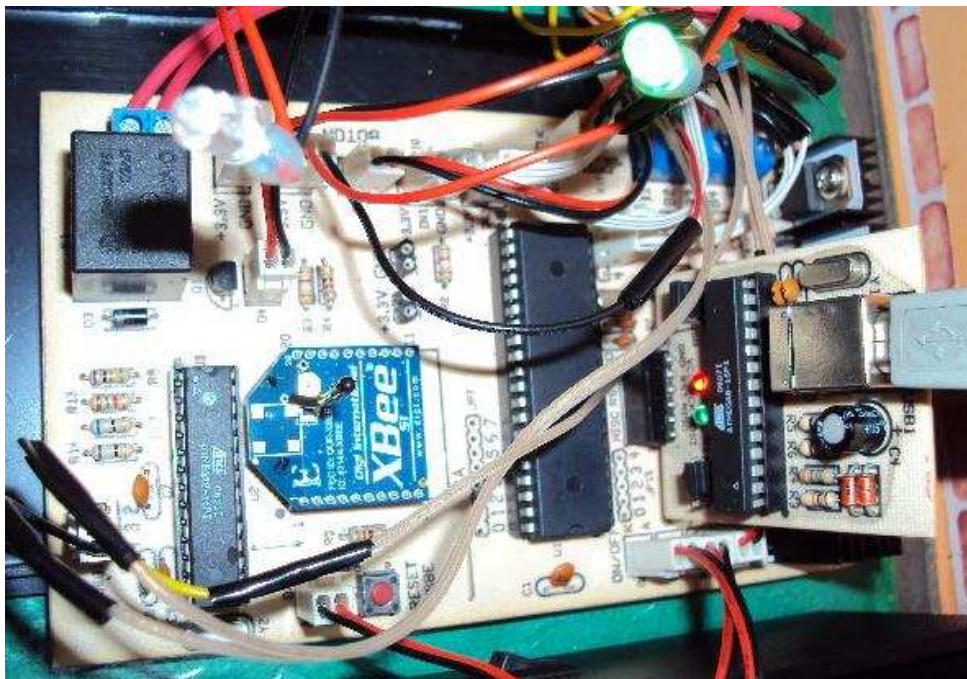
Tarjeta electrónica al final del proceso de soldadura
